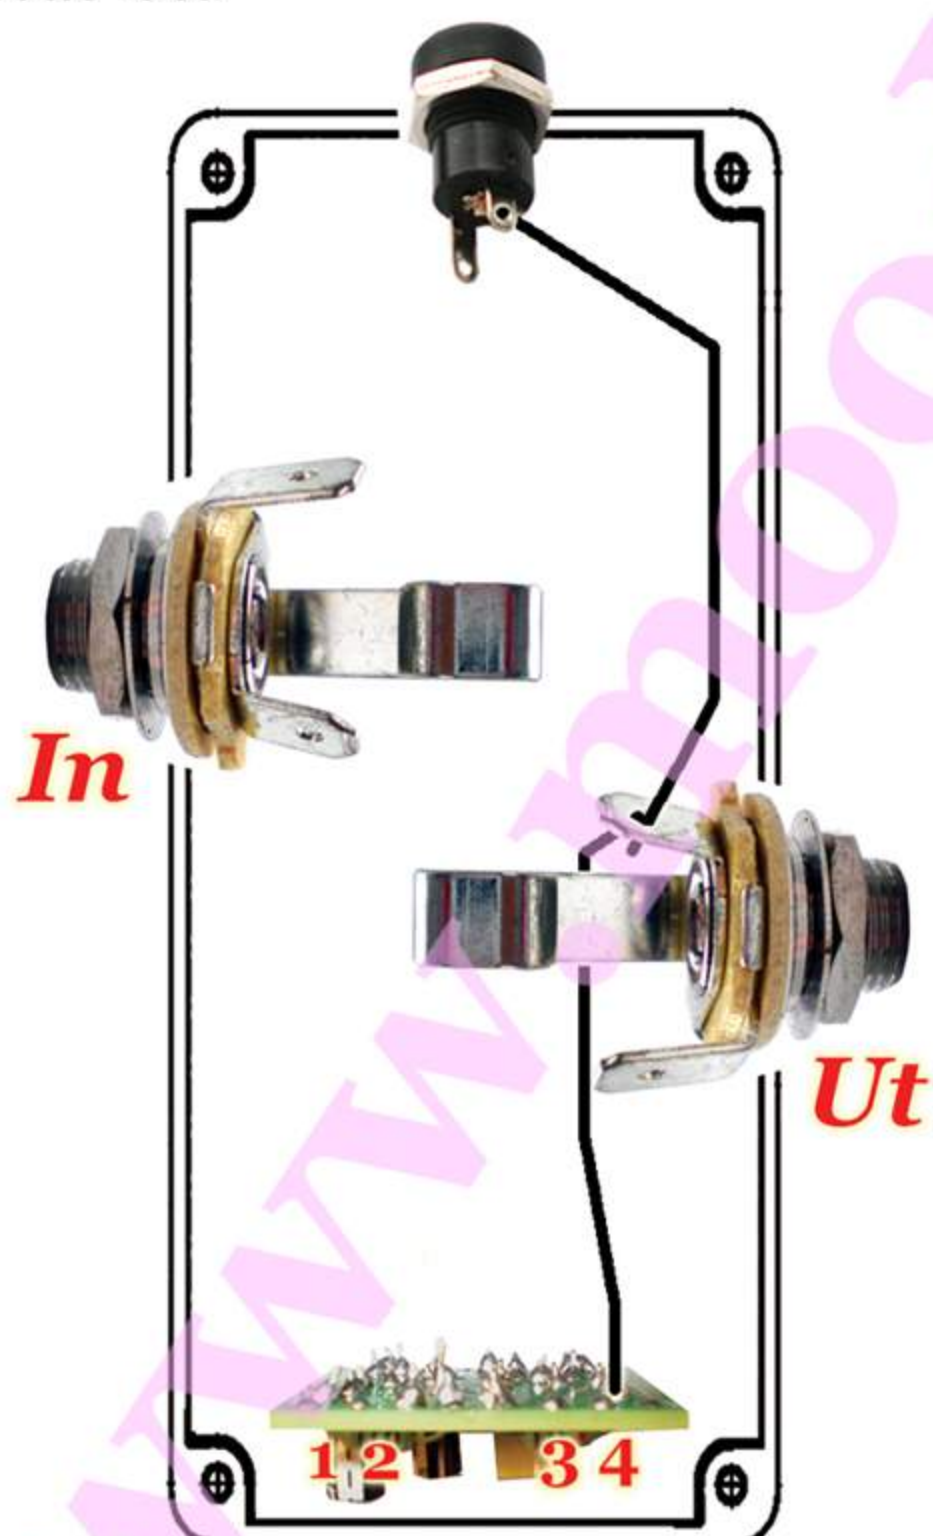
Jordsladdar mellan strömjack, utjack och kort.
